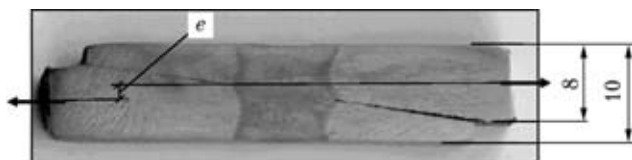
Макрошлиф (X1) сварного соединения деталей из стали 10 кп толщиной 8 + 8 мм, имеющего скосы по сопрягаемым поверхностям
